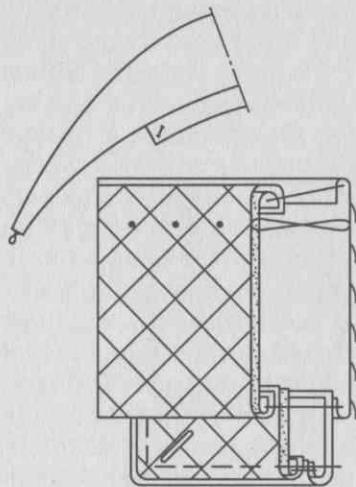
Схема сборки съемного шалевого воротника со свободными концами и притачной стойкой
